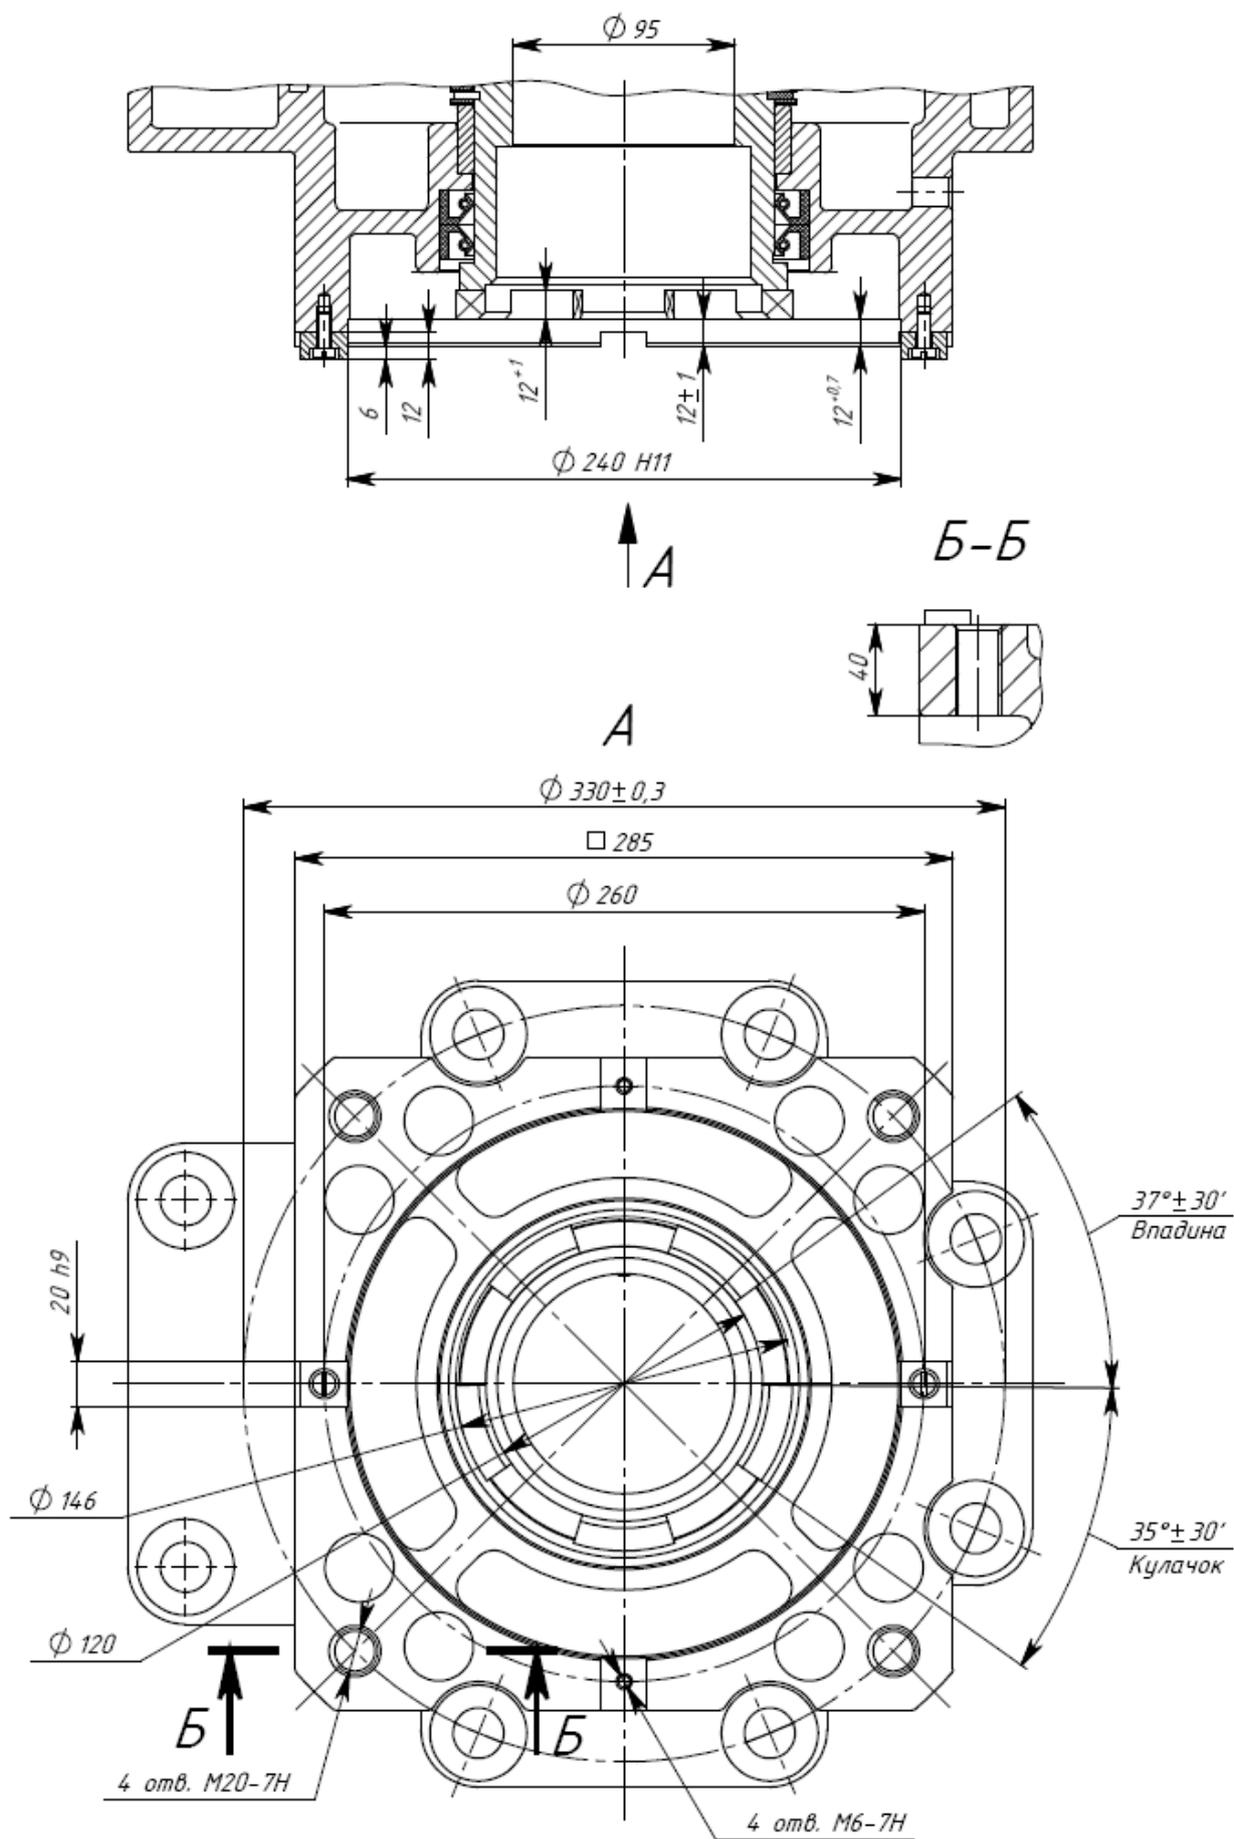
Присоединение типа Г для конструктивной схемы 43
